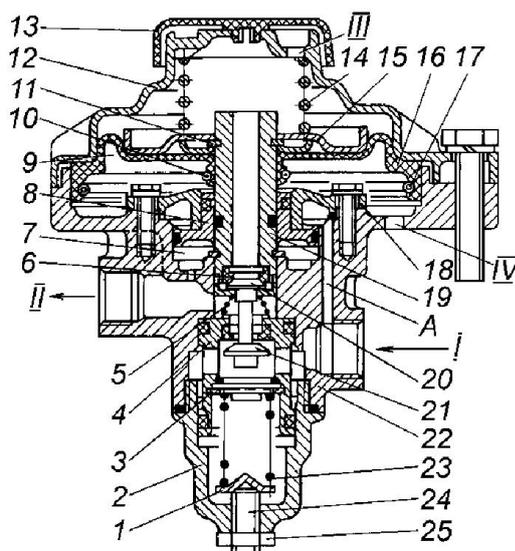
Клапан управления тормозными механизмами прицепа с однопроводным приводом:
